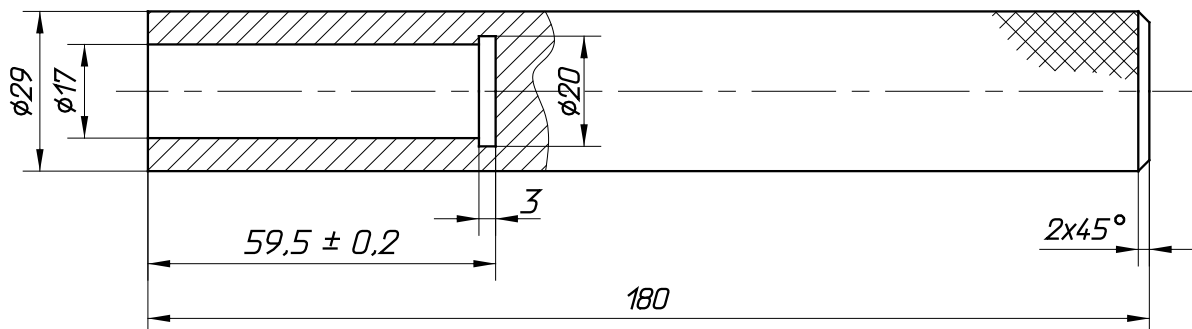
Оправка для запрессовки оси шкива в рычаг
